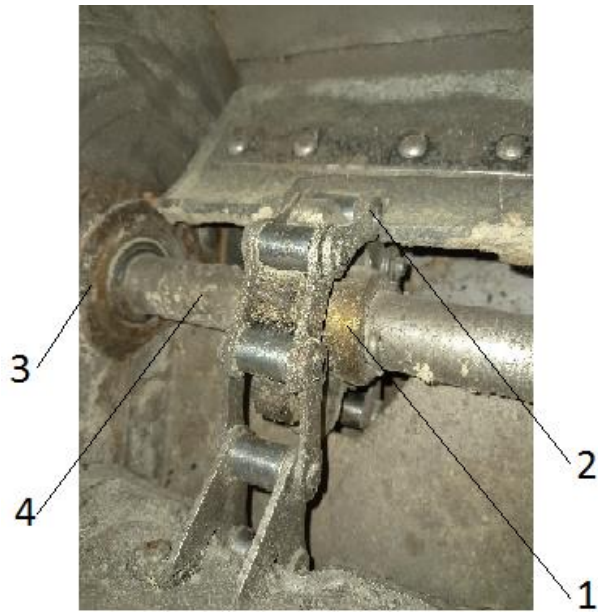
Верхня частина ланцюга зі скребками елеватора зернозбирального комбайна.
